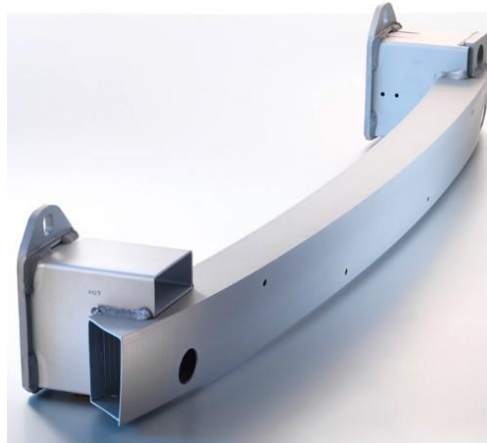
Viga de soporte de parachoques de aluminio extruido⁶⁰
